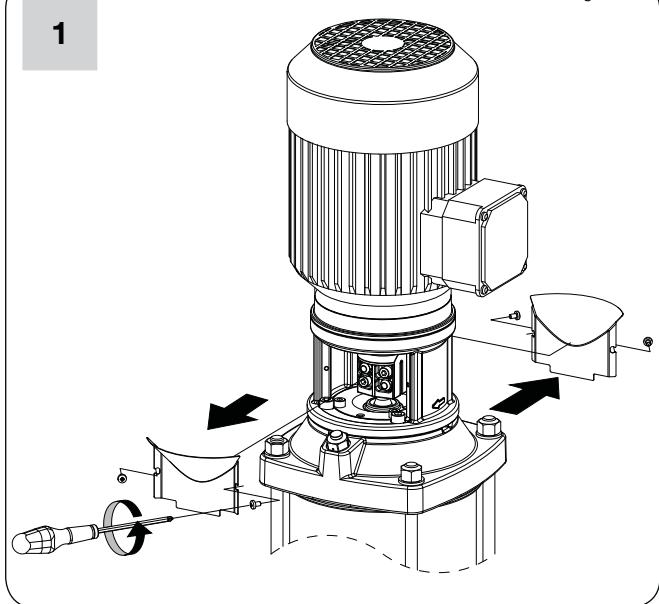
Remplacement du joint d'étanchéité – VR 3/5/9
